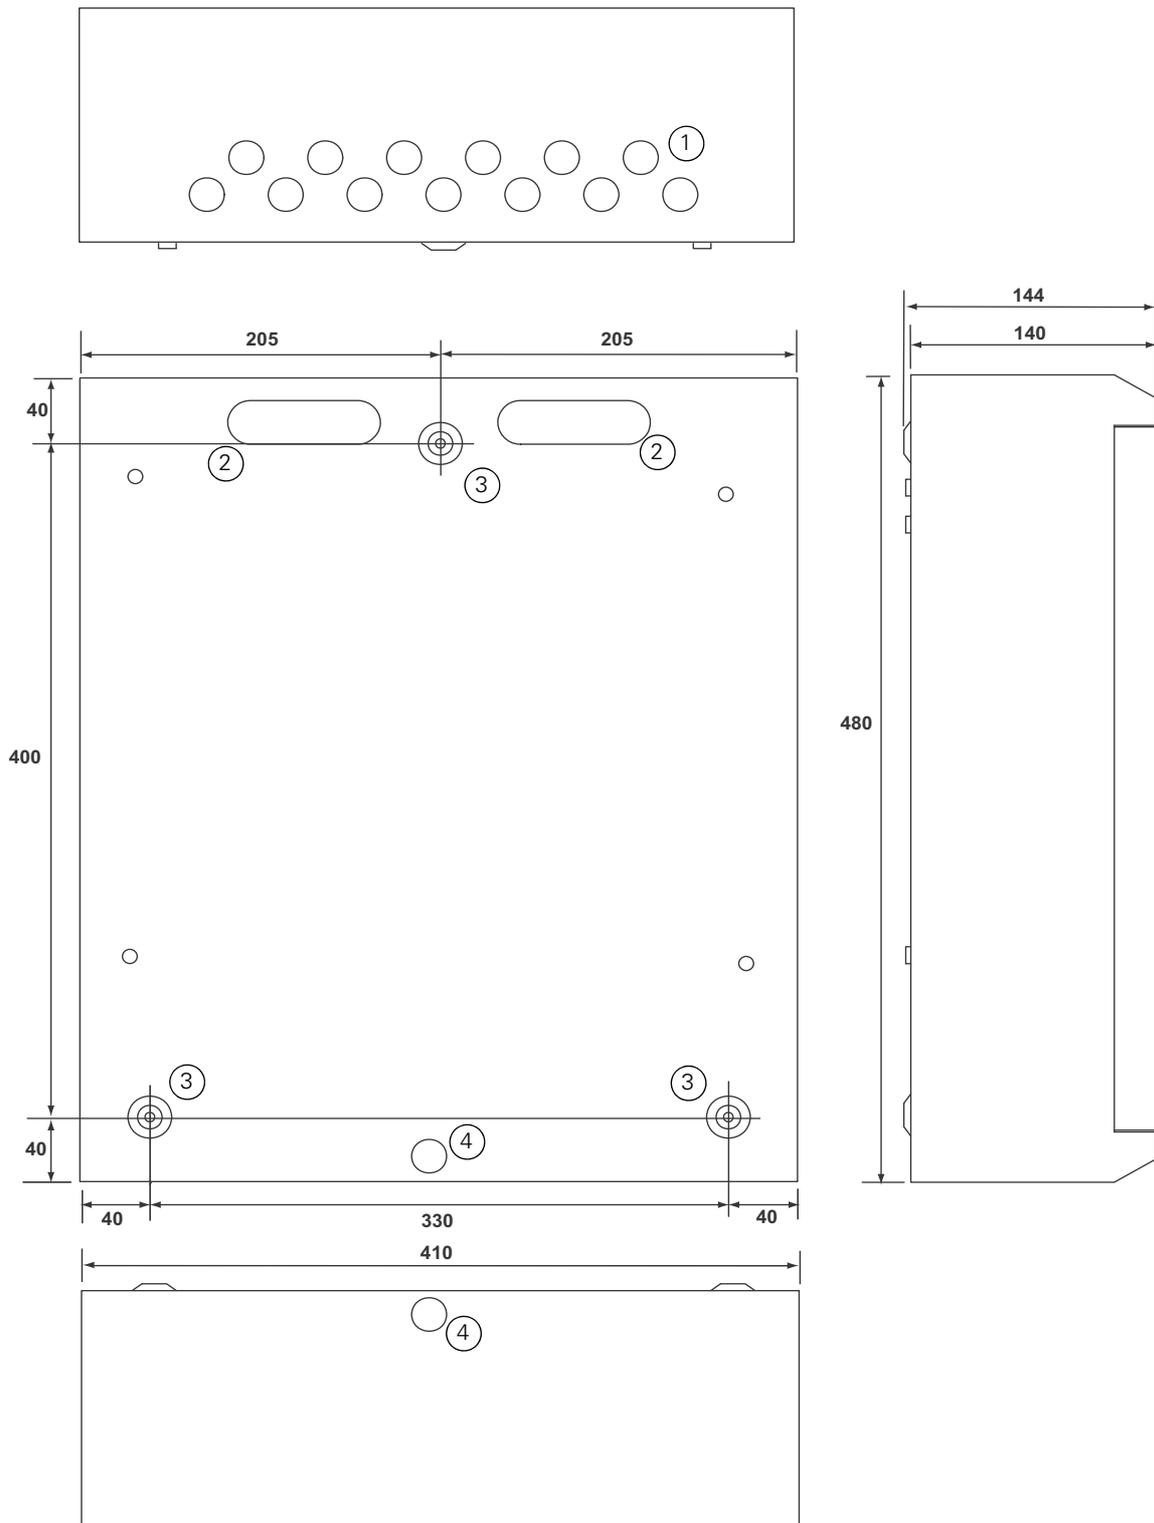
Dimensioni generali e di fissaggio – FIRECLASS 240-2
